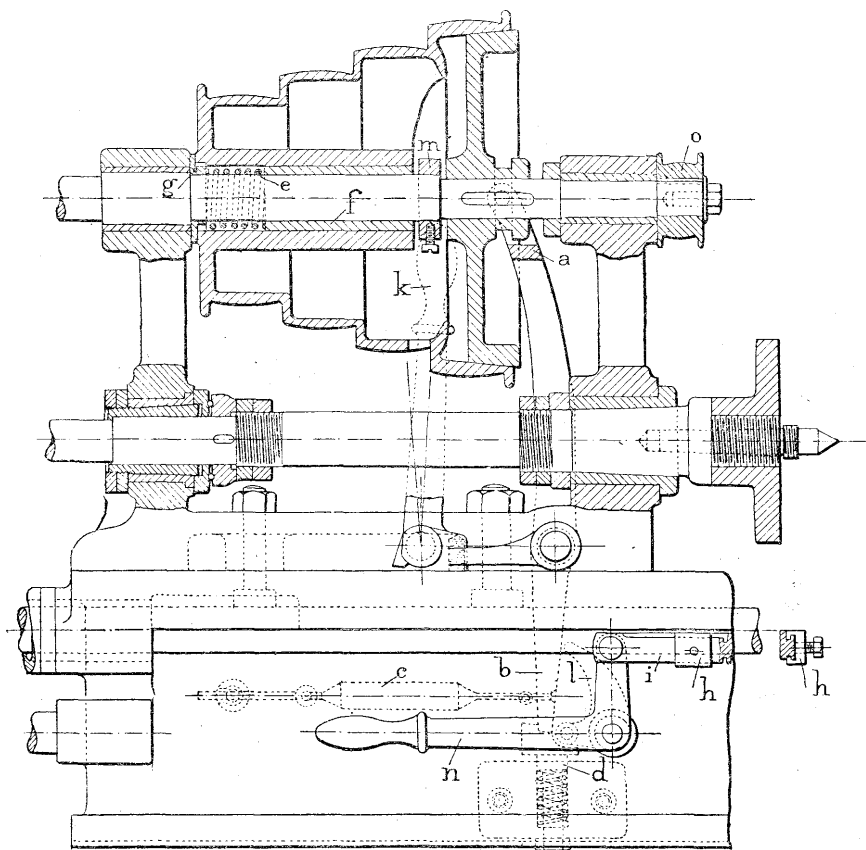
Poupée fixe du tour à boulons Reinecker.
